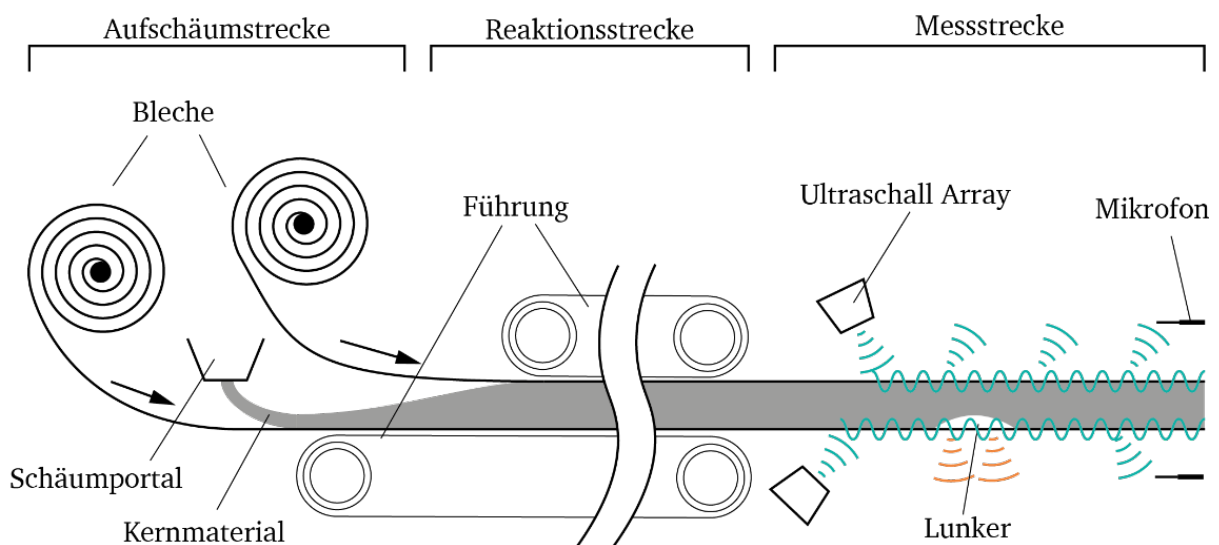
Schematische Darstellung einer kontinuierlichen Produktionsstrecke für Sandwichelemente und des möglichen Einbauortes des US-Systems
